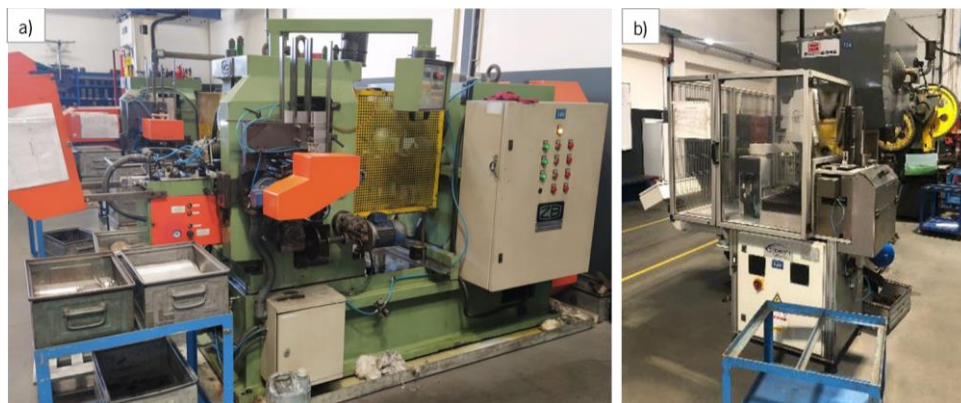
Laminador (a) e rebarbador automático (b) dispostos no Pavilhão 5
